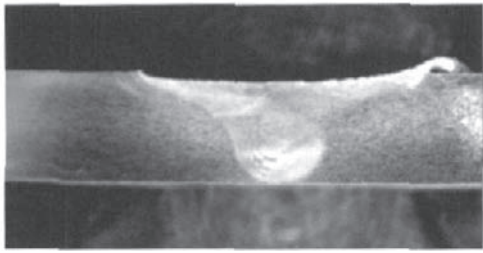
6061-T6铝合金搅拌摩擦焊接头横截面宏观形貌
